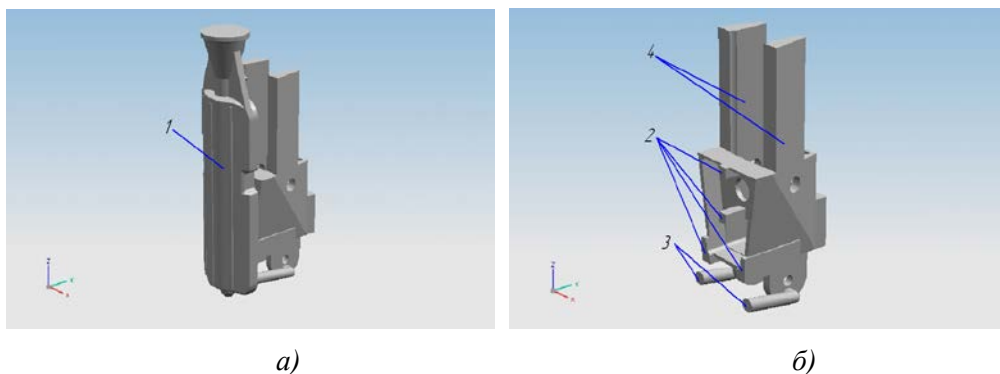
Трёхмерная модель отливки «Узел крепления»:
